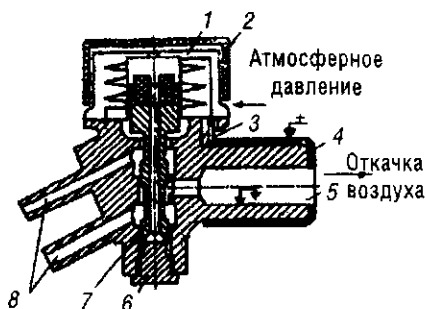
Схема электромагнитного пульсатора для попарного доения: 1 – электромагнит; 2 – кожух; 3 – металлическая оболочка; 4 – прокладка; 5 – патрубок; 6 – пробка; 7 – стержень; 8 – патрубки пульсирующего вакуума
